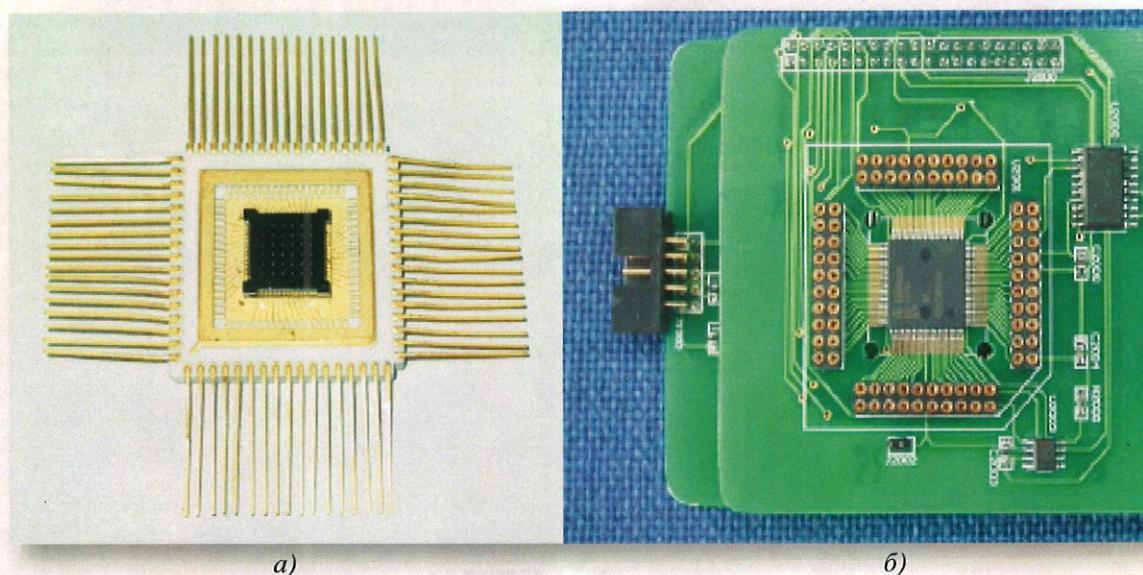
Общий вид комплекса РМДТТ и его вид в сборке для испытаний
